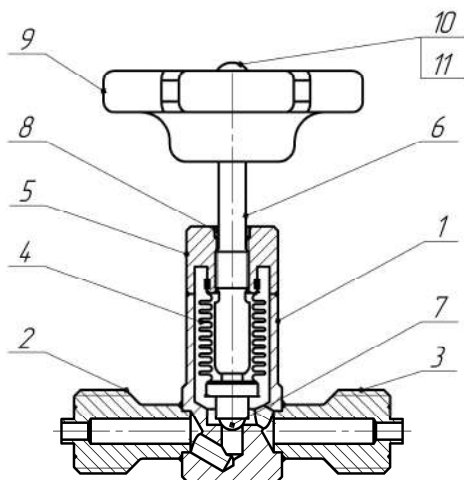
Конструктивная схема ВИГ6С: 1 – корпус; 2 – штуцер входа; 3 – штуцер выхода; 4 – сильфон; 5 – букса; 6 – шток; 7 – сферический наконечник; 8 – фторопластовая вставка; 9 – маховик; 10 – табличка «Откр-Закр»; 11 – гайка колпачковая
